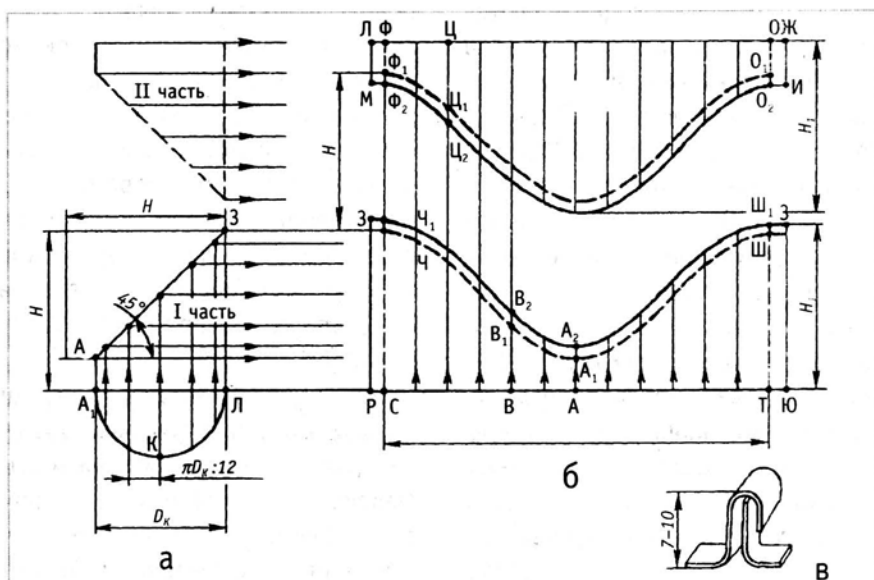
Построение разверток-заготовок прямого колена: а — прямое колено; б — заготовки прямого колена; в — отгиб кромок и соединение их в одинарный стоячий фальц
